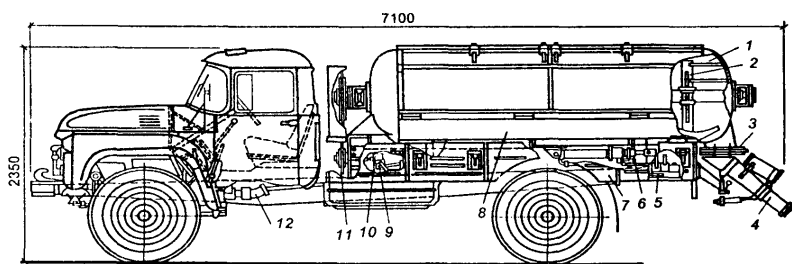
Авторастворовоз СБ-89В: 1 – цистерна в сборе; 2 – лопастной побудитель; 3 – фланец разгрузочной точки; 4 – дополнительный лоток; 5 – рукоятка включения привода побудителя; 6 – рукоятка управления механизмом запираания конвейера; 7 – рама шасси; 8 – выдвижной ленточный конвейер; 9 – блокирующий золотник; 10 – трехпозиционный гидрораспределитель; 11 – фланец; 12 – привод гидронасоса
